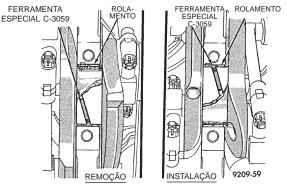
Remoção e Instalação do Rolamento Principal Superior com a Ferramenta C-3059
